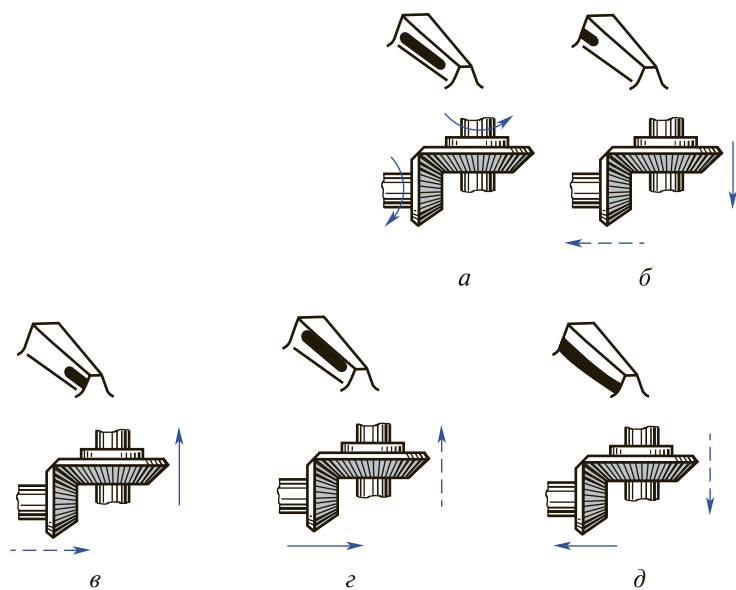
Схема регулировки зацепления конических шестерен главной передачи автомобиля:
